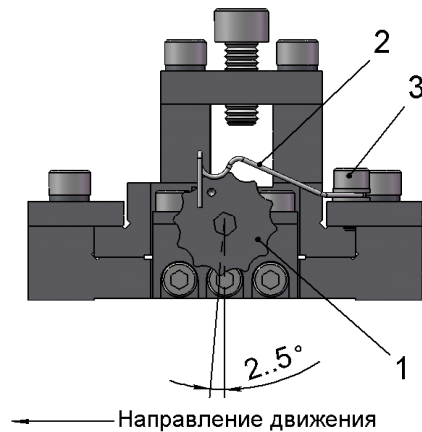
Проверка настройки пружины фиксатора звездочки винта подачи
